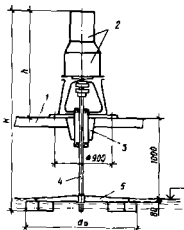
Аэратор механический поверхностный типа МП: 1 — рама; 2 — мотор-редуктор; 3 — муфта; 4 — вал; 5 — рабочий орган
